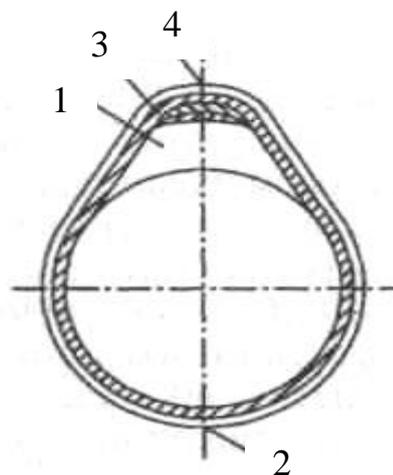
Схема расположения пастообразного припоя на поверхности ленты
